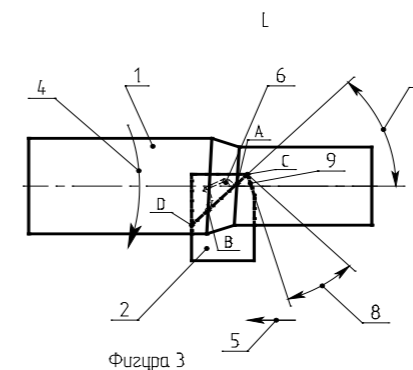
Взаимное положение резца и заготовки (вид L)
